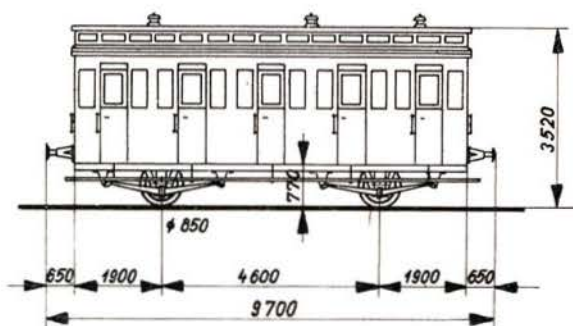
Stadtbahnwagen 3. Klasse aus dem Jahre 1882
